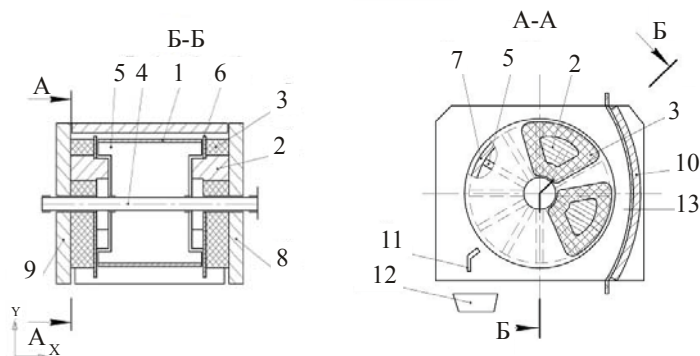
Принципова схема електромагнітного сепаратора: 1 — барабан у зборі; 2 — секторні виступи; 3 — котушка намагнічування; 4 — вал; 5 — концентратори магнітного поля; 6 — торцева шайба; 7 — немагнітна обичайка; 8 — боковина права; 9 — боковина ліва; 10 — феромагнітний екран; 11 — скребок; 12 — бункер; 13 — робочий зазор
